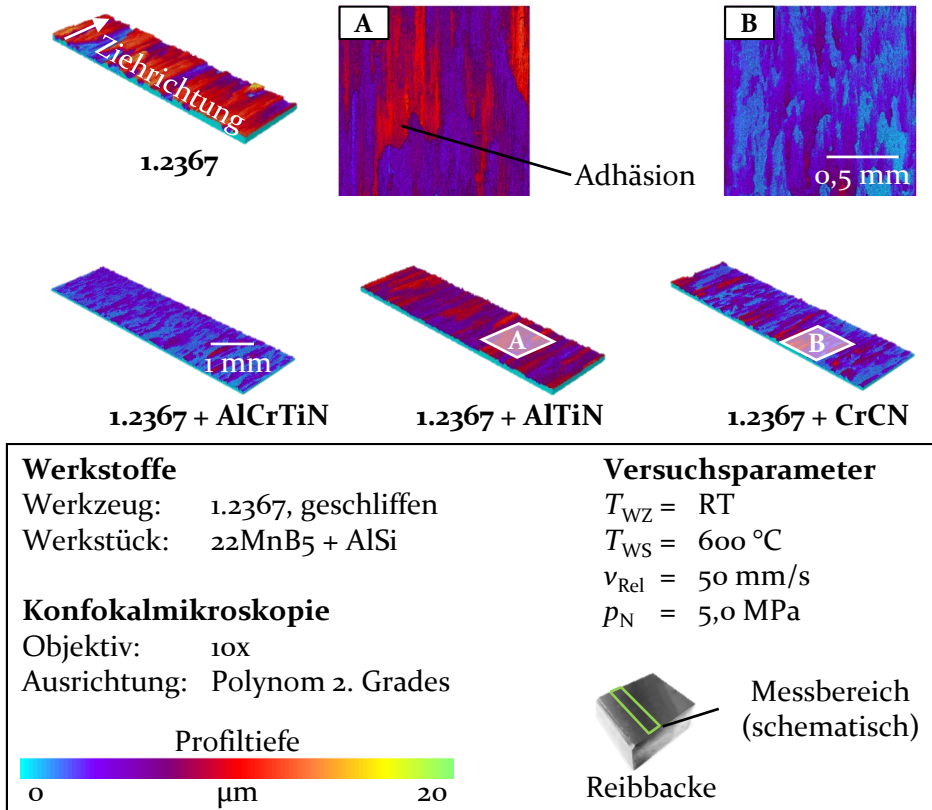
Topographiaufnahmen der Werkzeugoberfläche für unterschiedliche Werkzeugbeschichtungen
